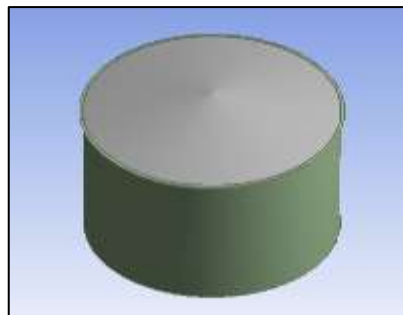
TANQUE DE ALMACENAMIENTO DE AGUA CALIENTE, DISEÑO DE FORMA
